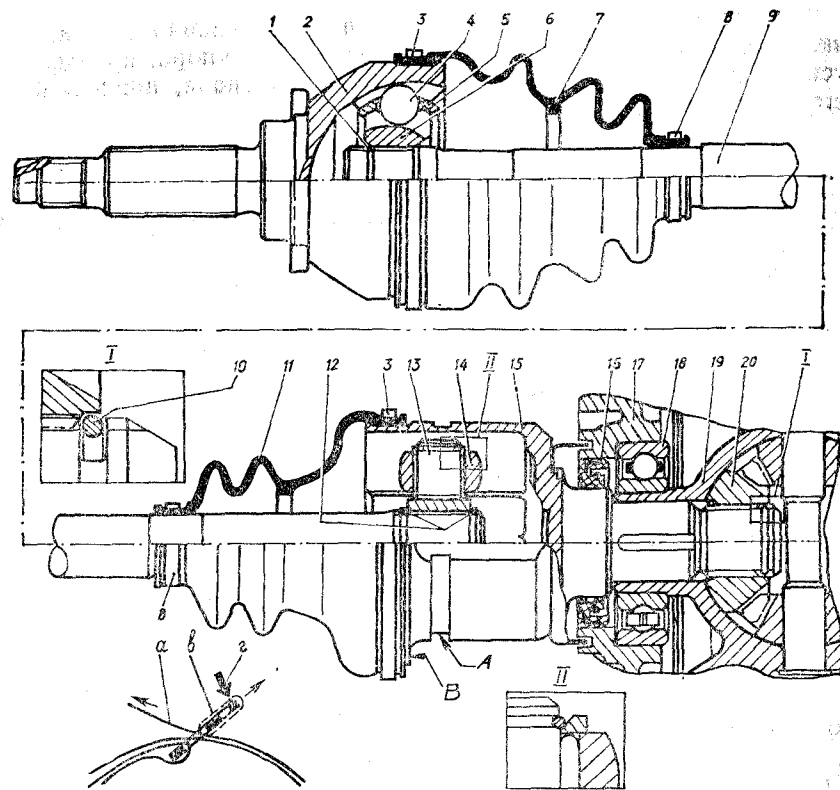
Шарнирный вал и его закрепление в шестерне дифференциала:
